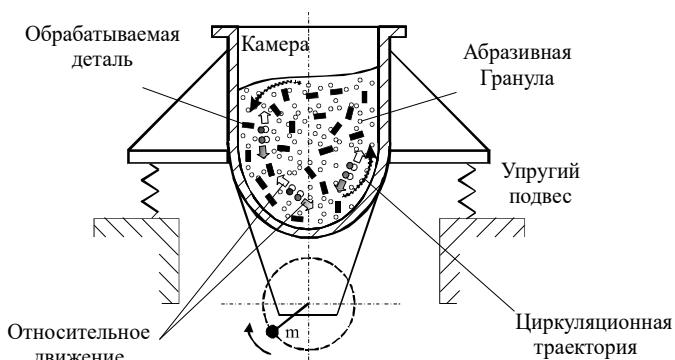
Схема станка для виброабразивной обработки с U-образной камерой
